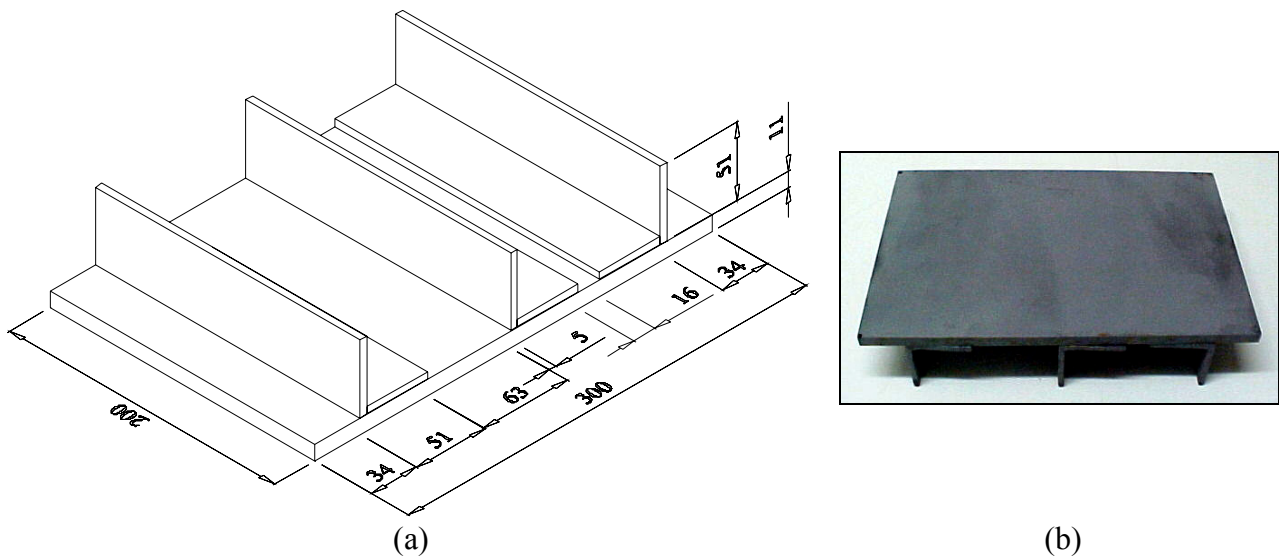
Placa retangular com enrijecedores (dimensões em mm).
